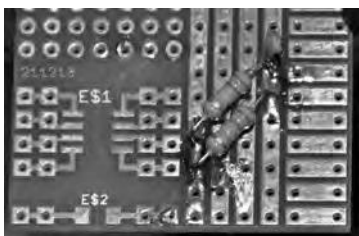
La piccola saldatura può essere rimossa con il saldatore..
